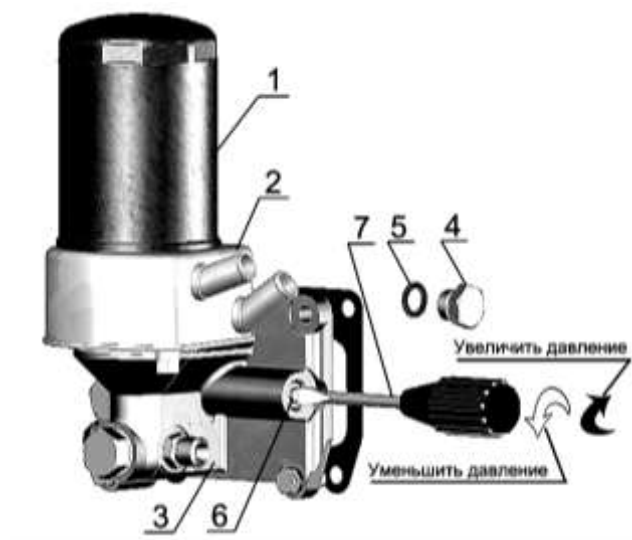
Регулировка давления масла: 1 – фильтр масляный; 2 – жидкостно-масляный теплообменник; 3 – корпус масляного фильтра; 4 – пробка клапана; 5 – прокладка пробки; 6 – пробка регулировочная; 7 - отвертка
